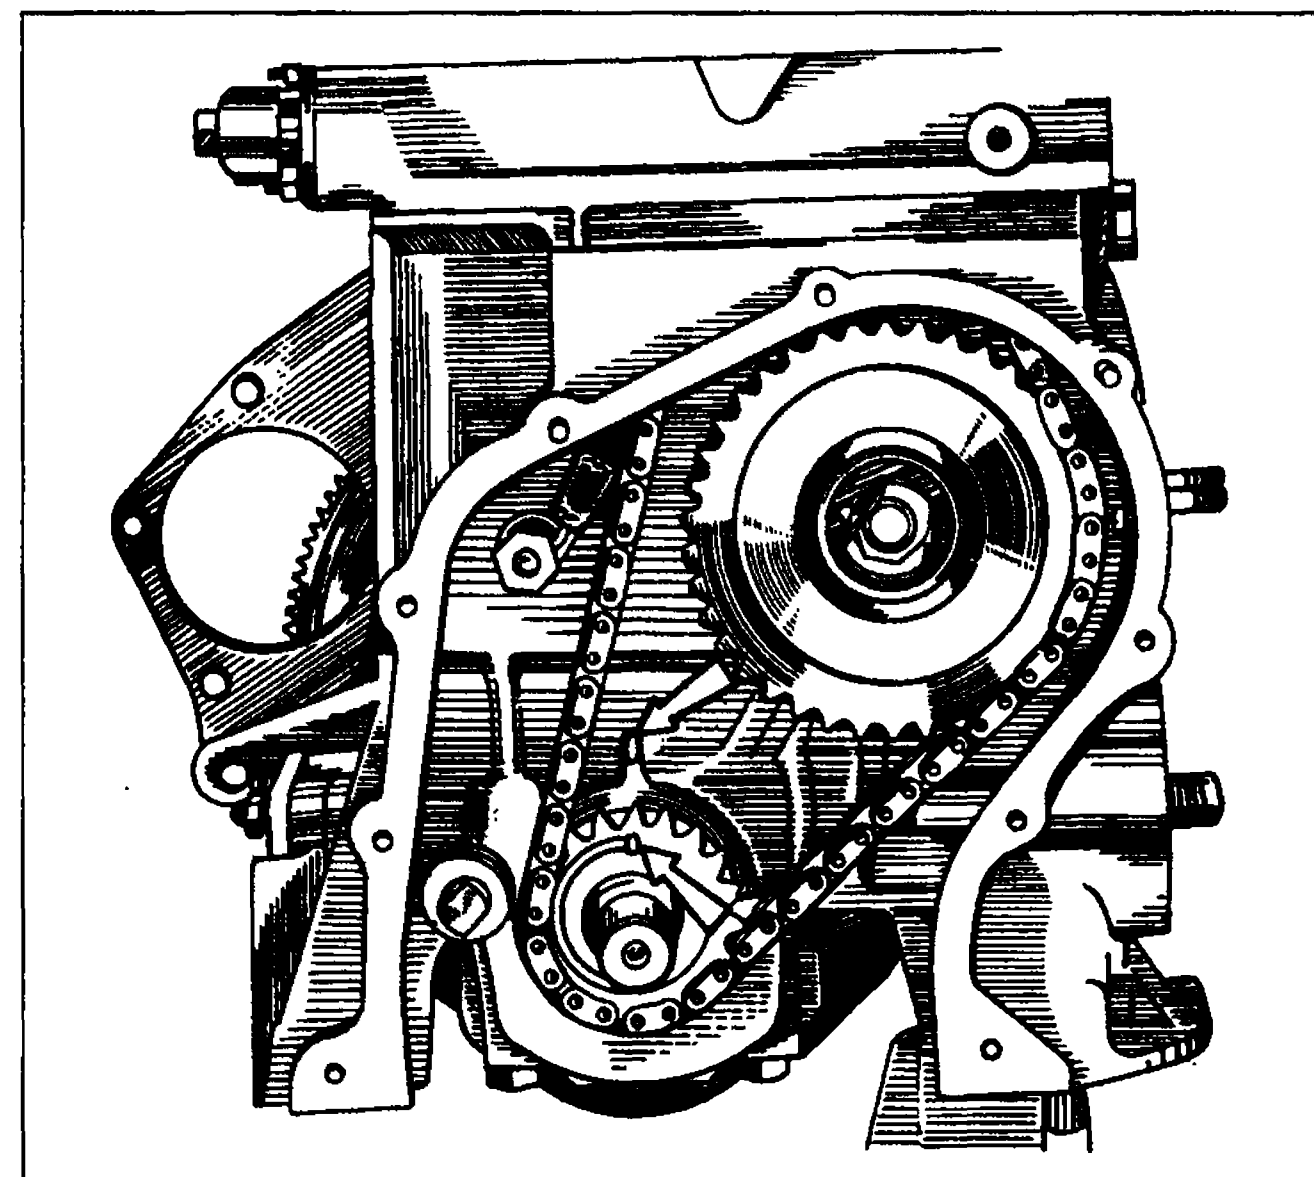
Проверка совпадения установочной метки на звездочке коленчатого вала с меткой на блоке цилиндров
